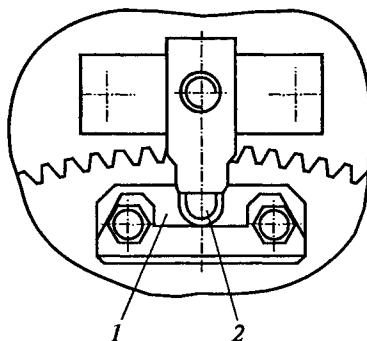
Устройство фиксации траверсы электродвигателя ДТК-800КЭ:
